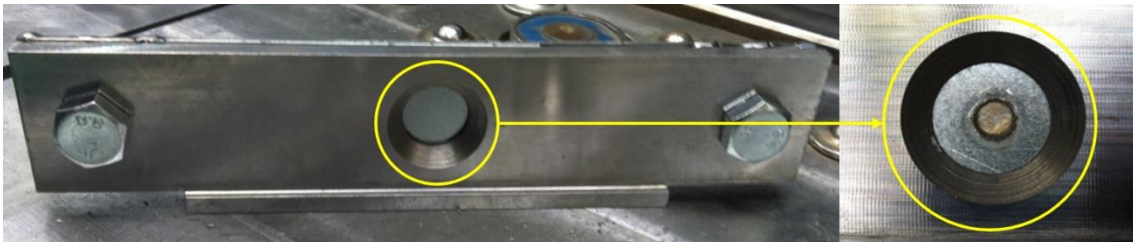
Plantilla para realizar los puntos de soldadura
